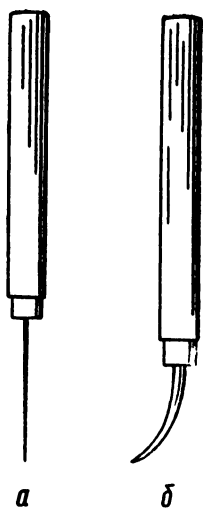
Инструменты для чеканки: а — чертилка; б — давьльник.
